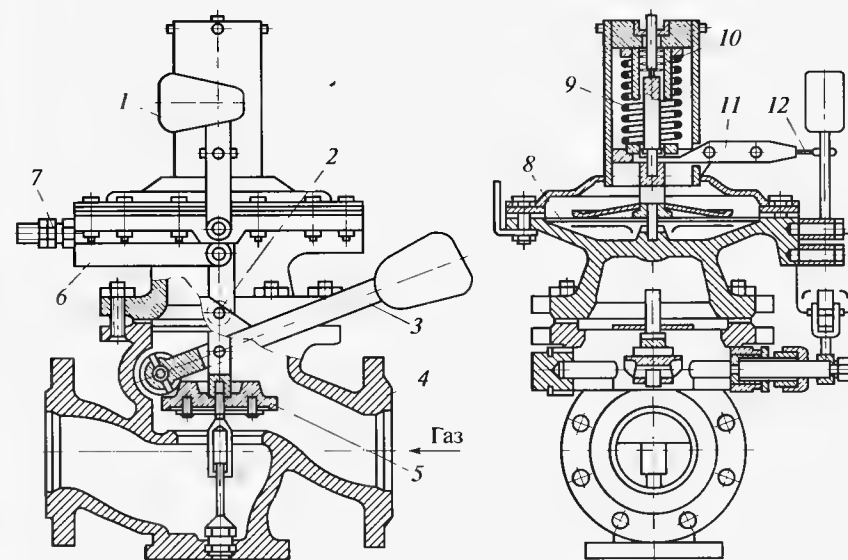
Предохранительно-запорный клапан низкого (ПКН) и высокого (ПКВ) давления:
